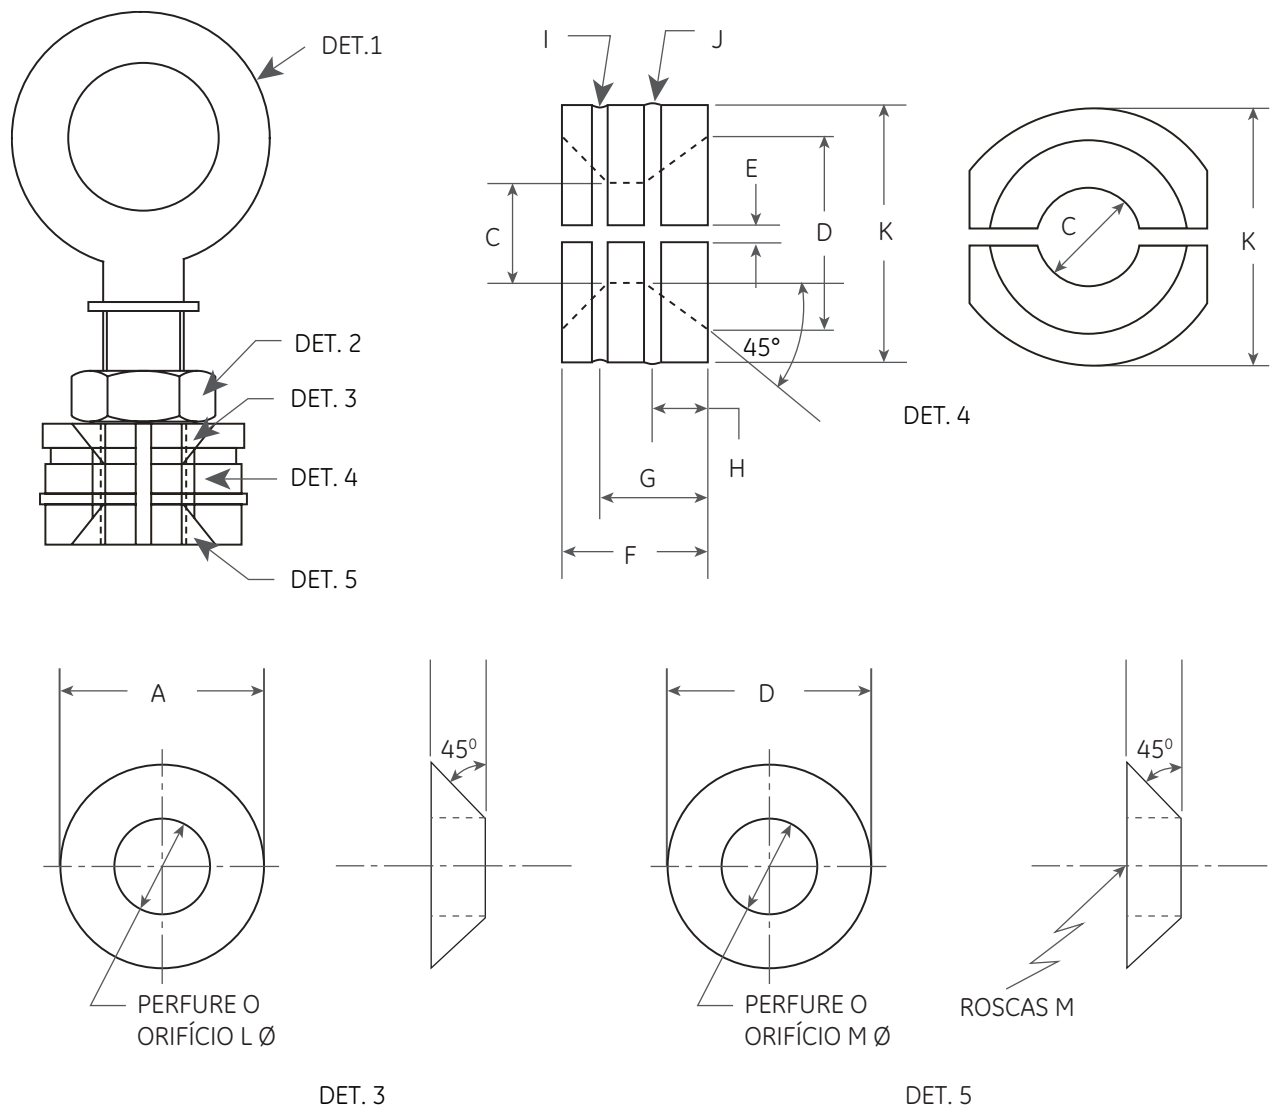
Suporte de disco e ferramenta de remoção e montagem de guia
